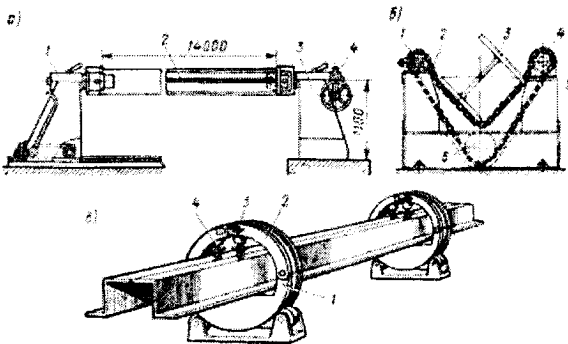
Схеми позиціонерів – кантавачів для зварювання балок
